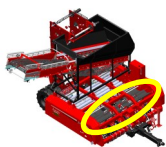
Рок Paddle и твердых Paddle корректировки
